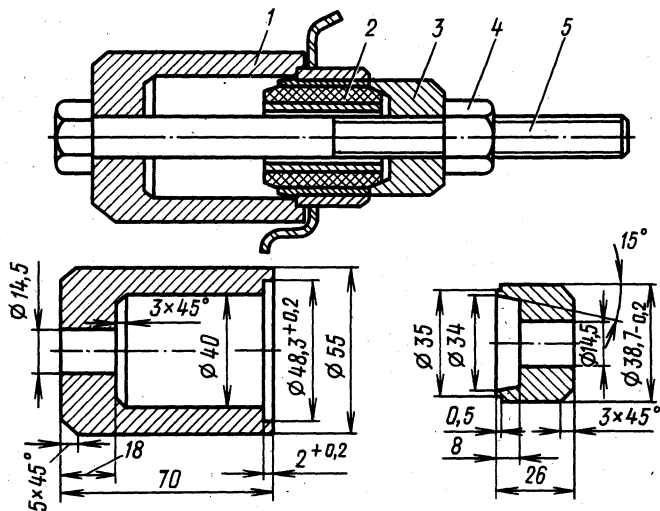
Приспособление для замены резинометаллических шарниров нижнего рычага передней подвески автомобиля «Москвич»:
